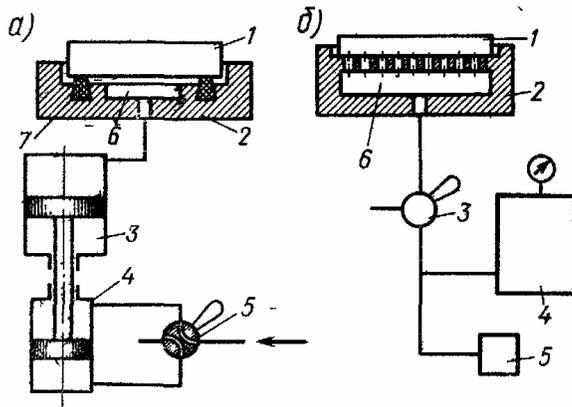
Схемы приспособлений с вакуумным приводом (а – с применением пневмоцилиндра; б – применением вакуумного насоса)
